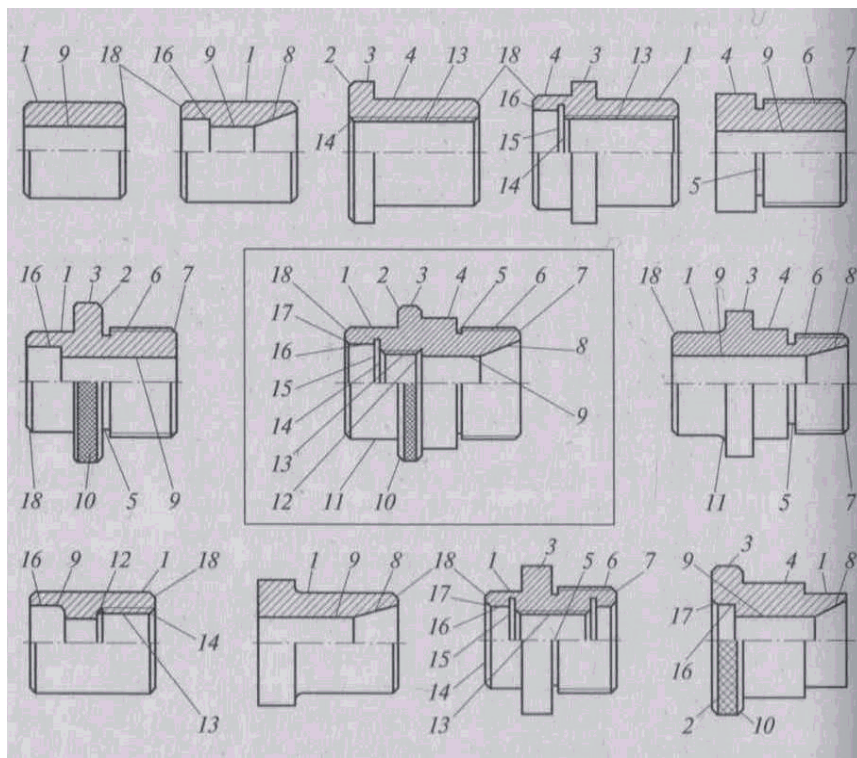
Комплексная деталь и детали ее группы, изготавливаемые на токарно-револьверном станке
